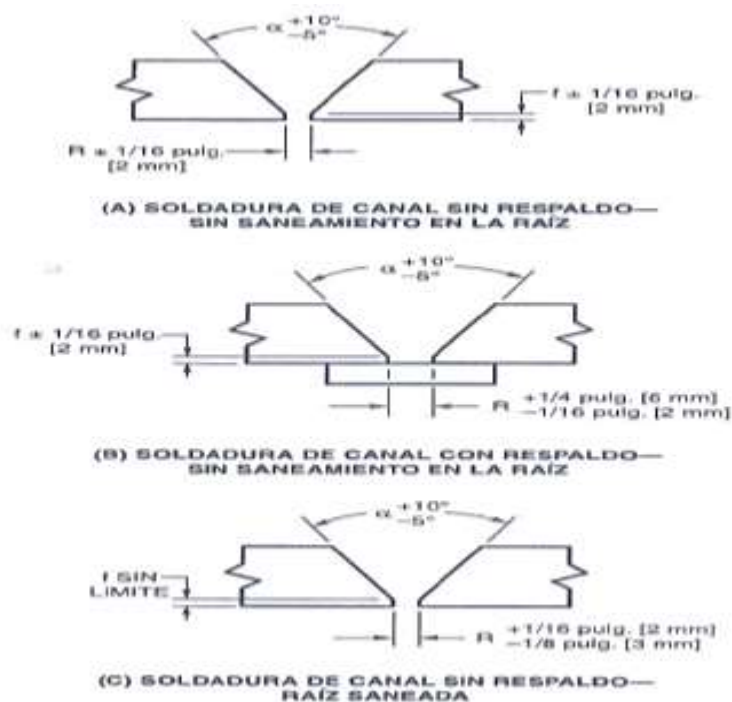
Tolerancia de las dimensiones de la junta
